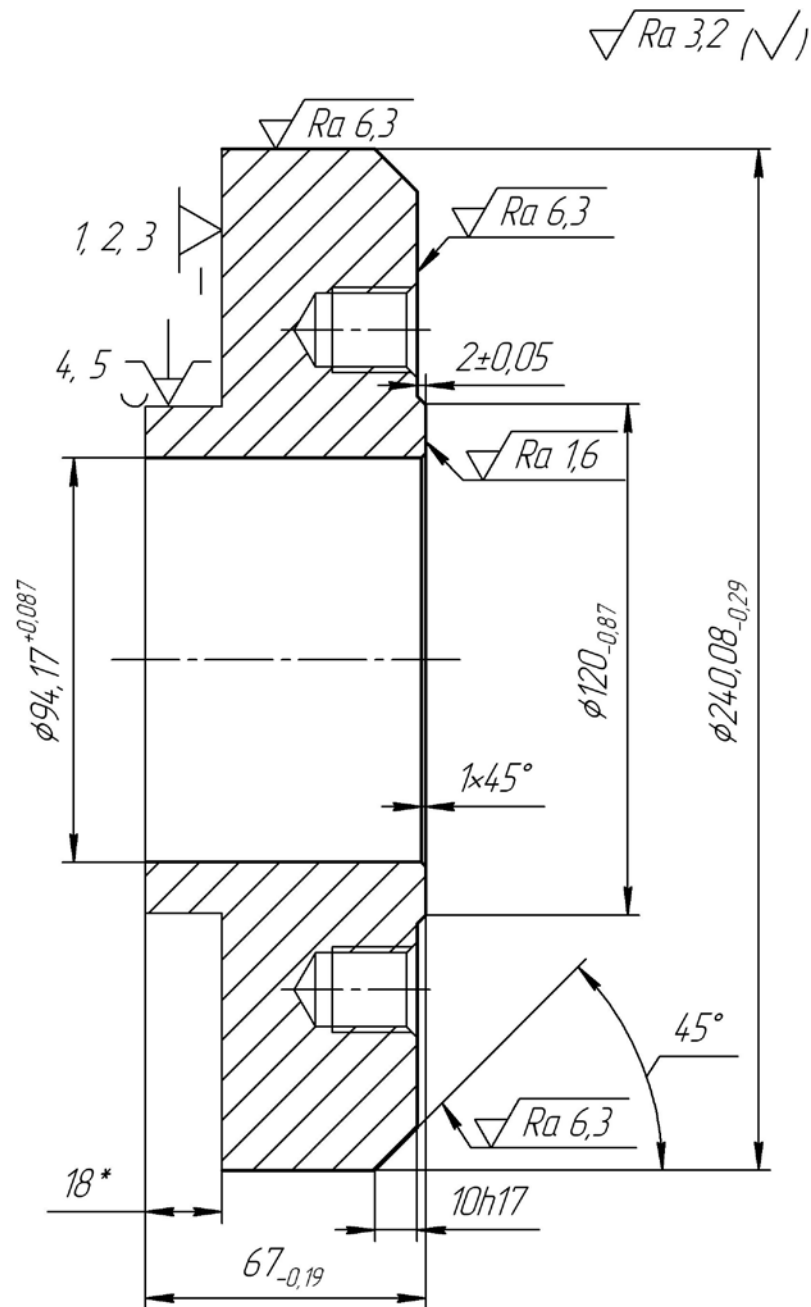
Альтернативна схема базування заготовки на операції 045 токарній з ЧПК
